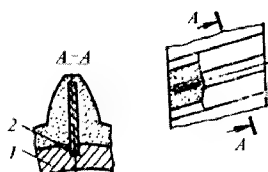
Зубчатый шевер для обработки крупномодульных зубчатых колес:
